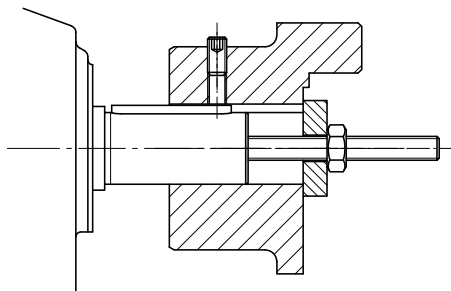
Beispiel einer einfachen Aufziehvorrichtung
